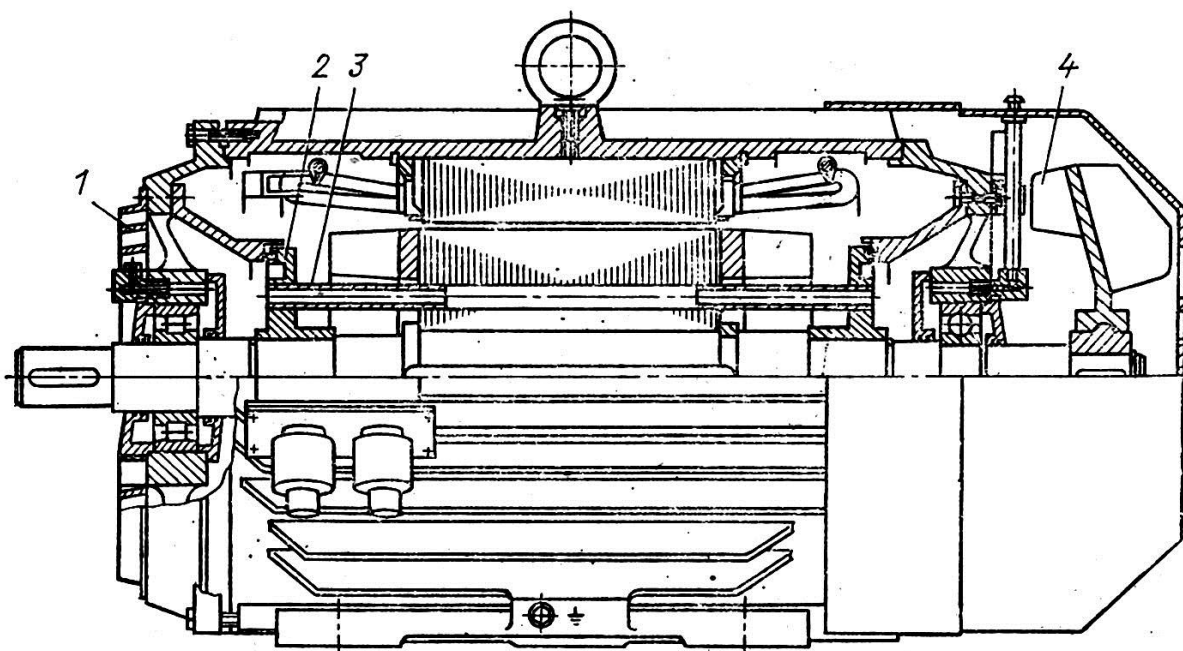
Асинхронный двигатель с короткозамкнутым ротором 4A280:
